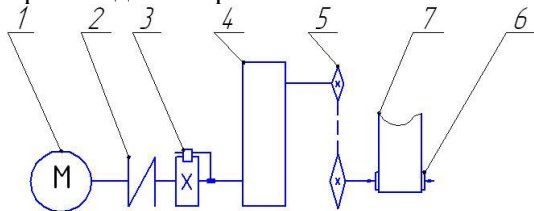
Схема приводу ківшевого елеватора: 1 – двигун; 2 – пружна муфта; 3 – стопорний пристрій (храповий); 4 – редуктор; 5 – ланцюгова передача; 6 – приводний барабан; 7 – стрічка
